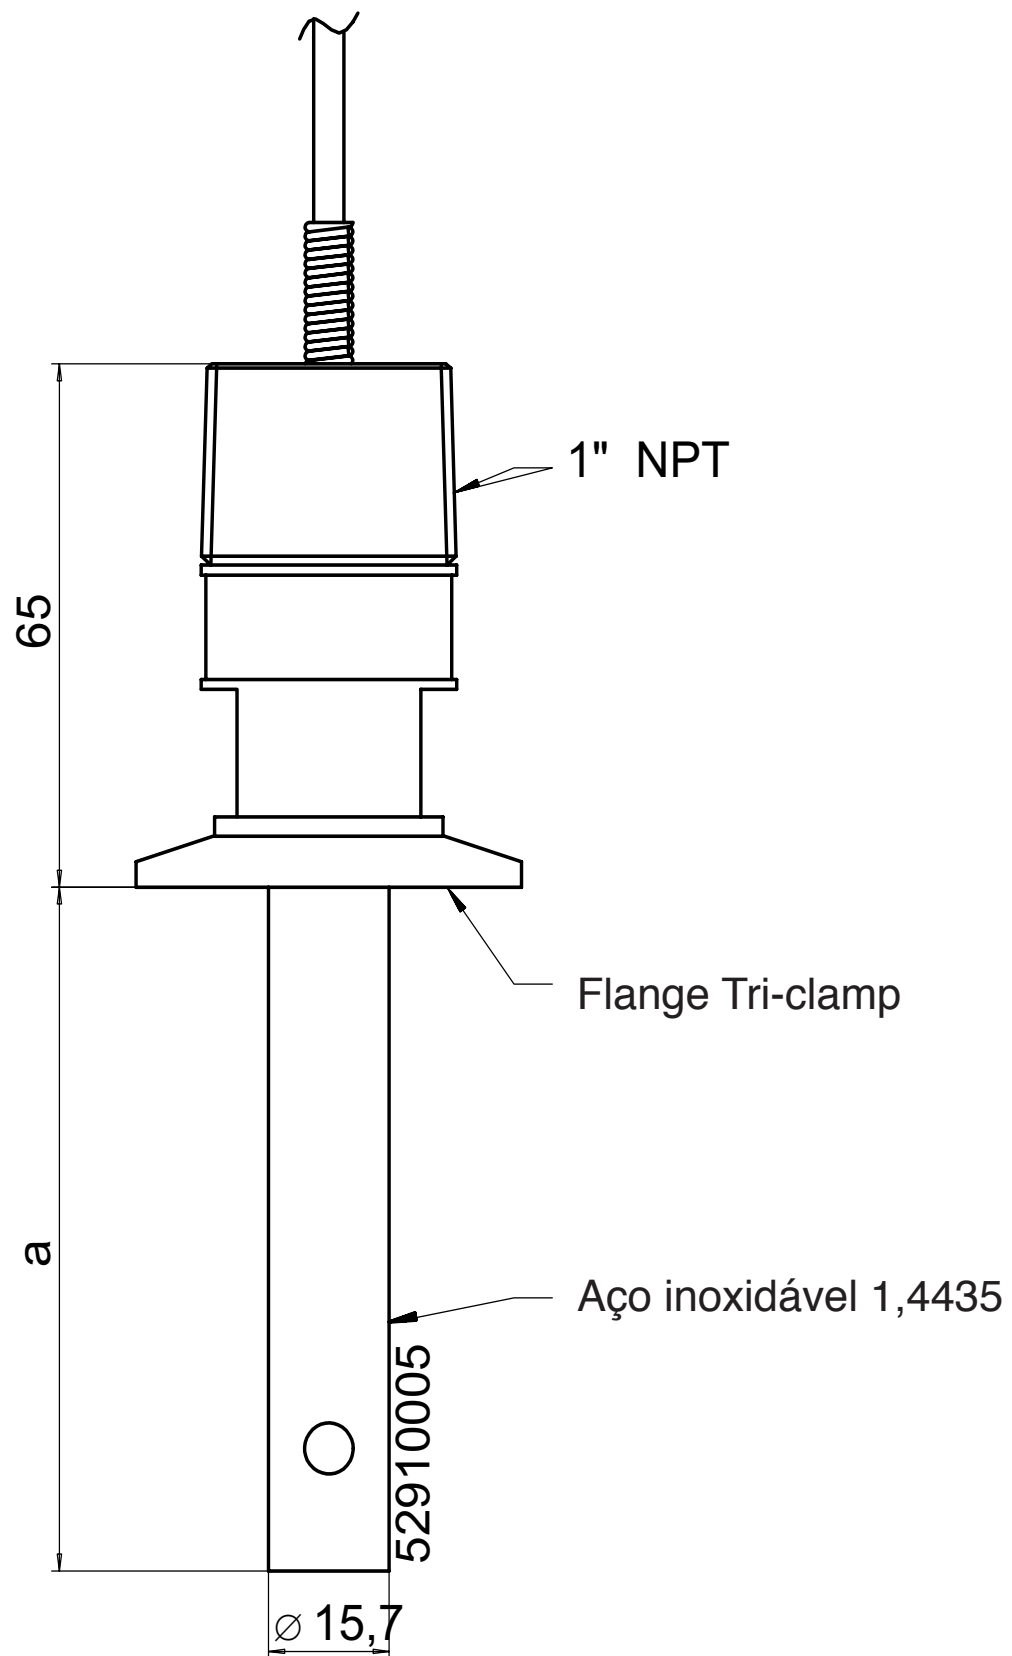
Desenho das dimensões do InPro[®]7001 com 2 eletrodos
